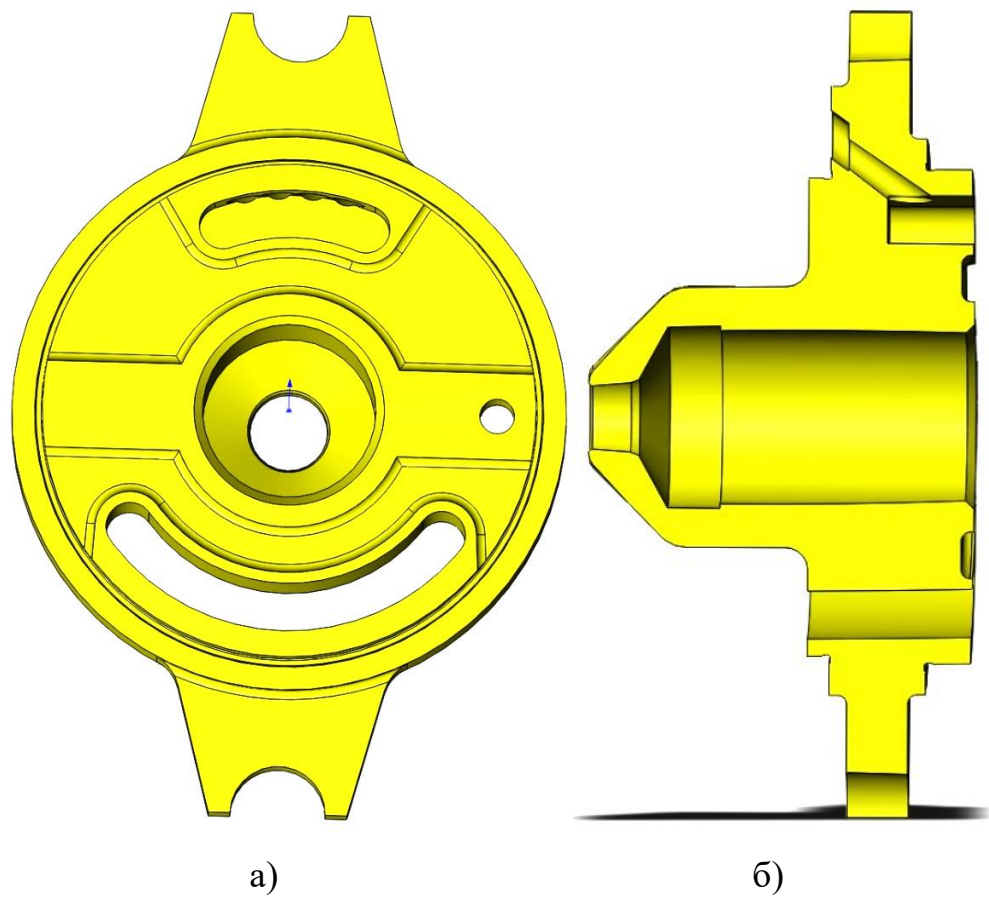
конструкція гнізда клапанної коробки: а – вид з заду, б – переріз
